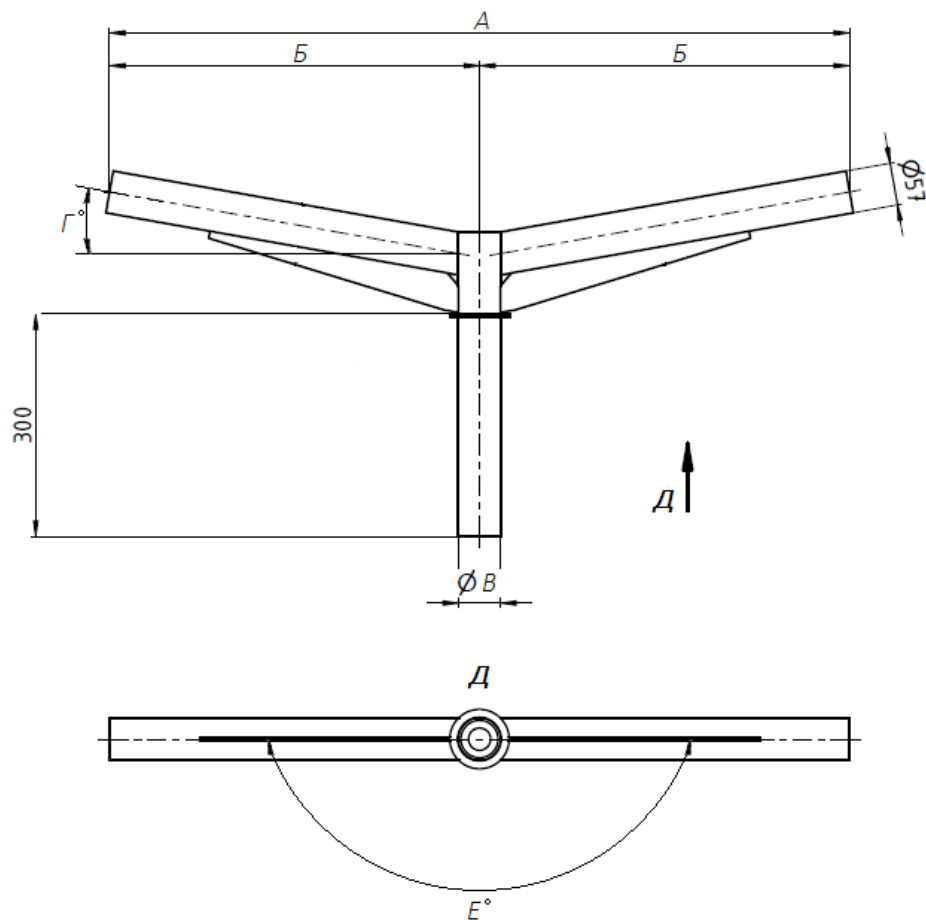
Габаритные и присоединительные размеры кронштейнов исполнений:
